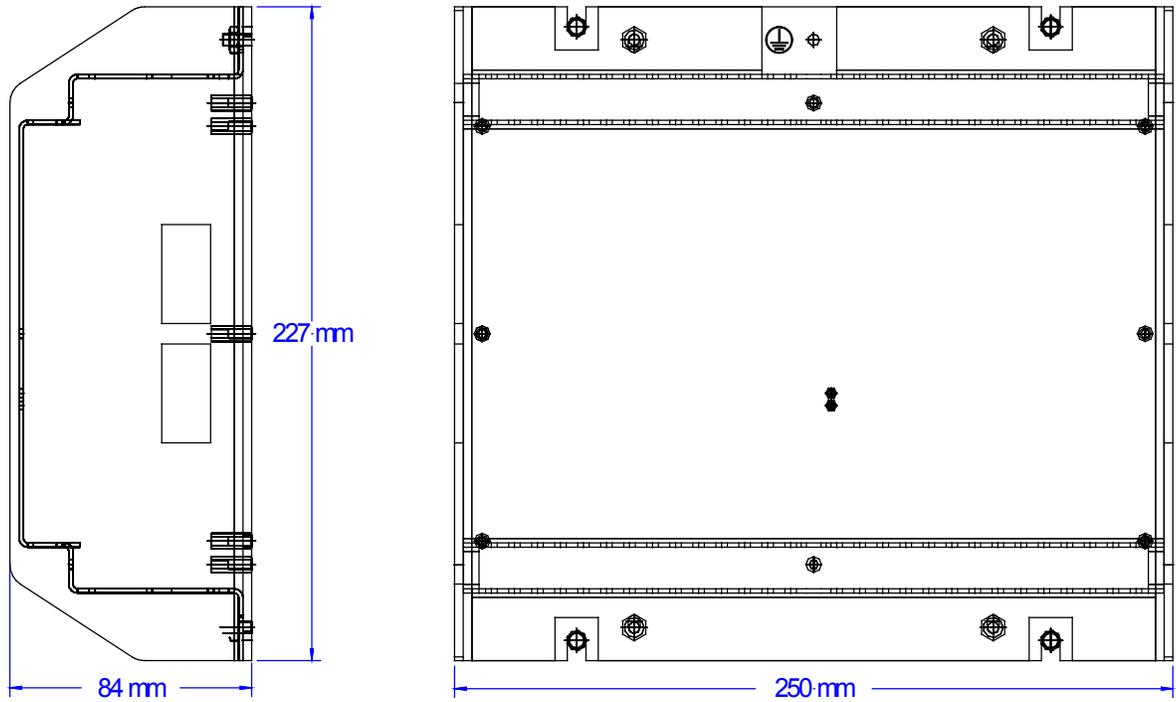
Metallgehäuse easYgen-3100 - Abmessungen
